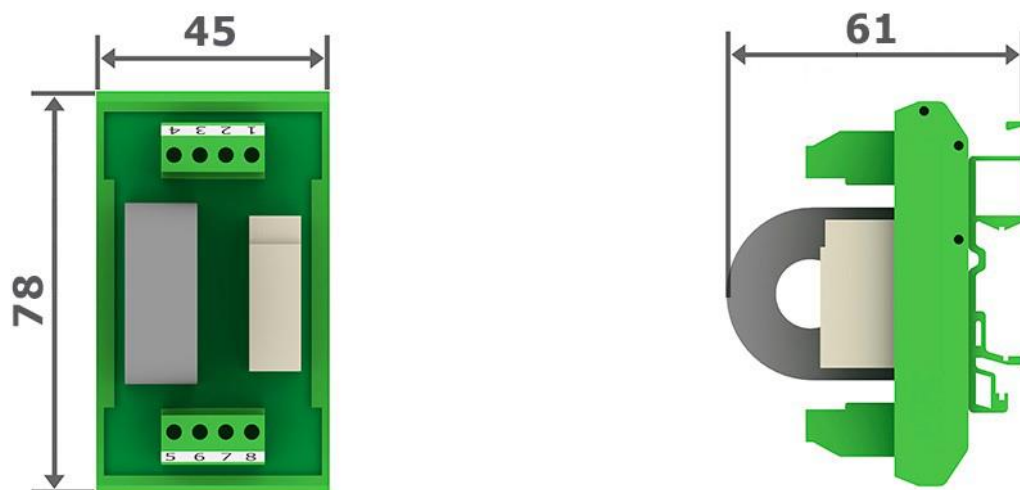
Габаритные и установочные размеры YCO – I
